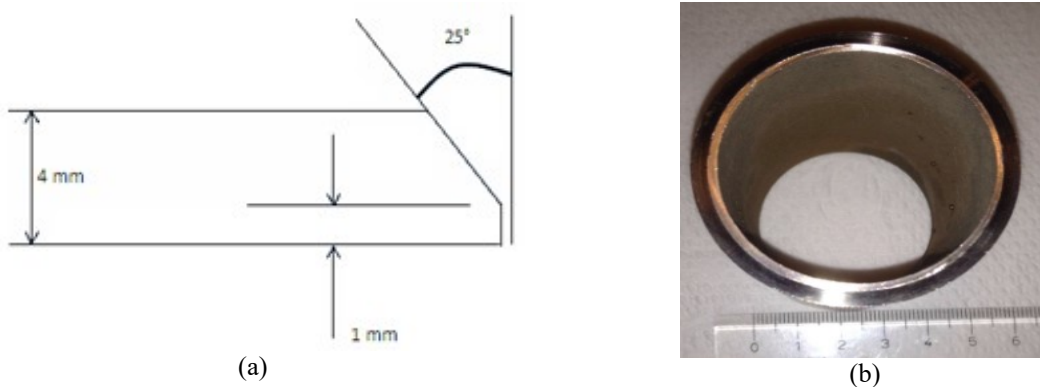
Detalhamentos dos tubos preparados para soldagem. (a) Detalhamento do chanfro utilizado na preparação para soldagem. (b) Detalhamento do tubo com diâmetro de 48,05 mm.
